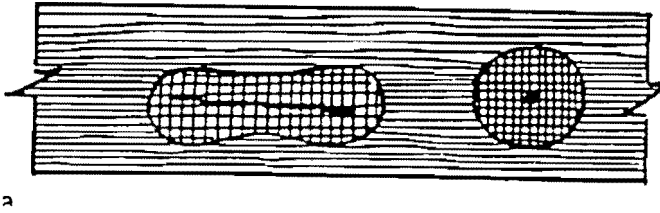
Ojos de pescado en una probeta de tracción: fractura frágil, con un defecto en el centro, rodeada de una zona de fractura dúctil.
